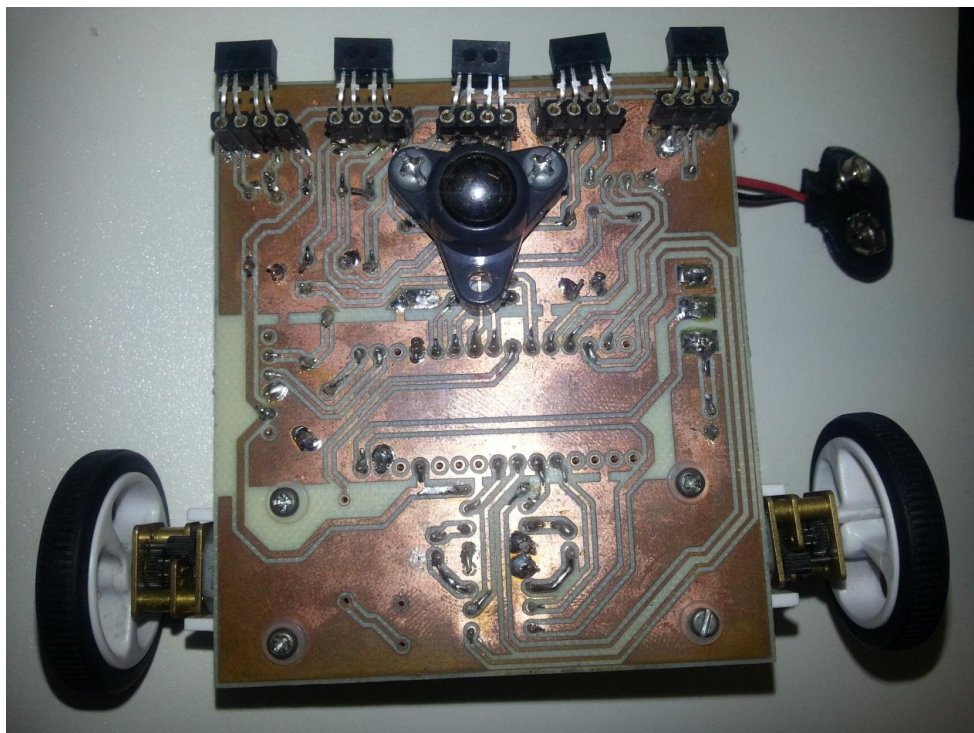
Vista posterior PCB soldado y montado
